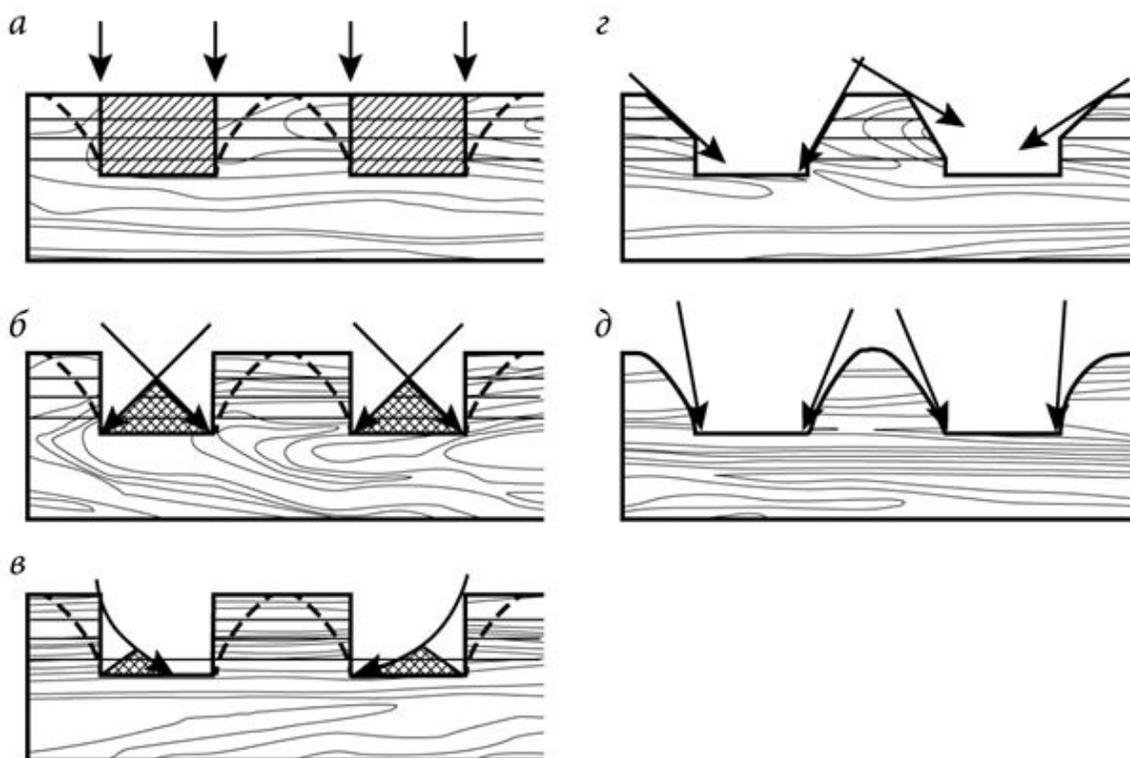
Последовательность выполнения рельефной резьбы (стрелками показано направление движения резца): а – надрез по контуру; б – подрезка к основанию надреза; в – выборка фона начерно; г – заоваливание; д – зачистка фона.
